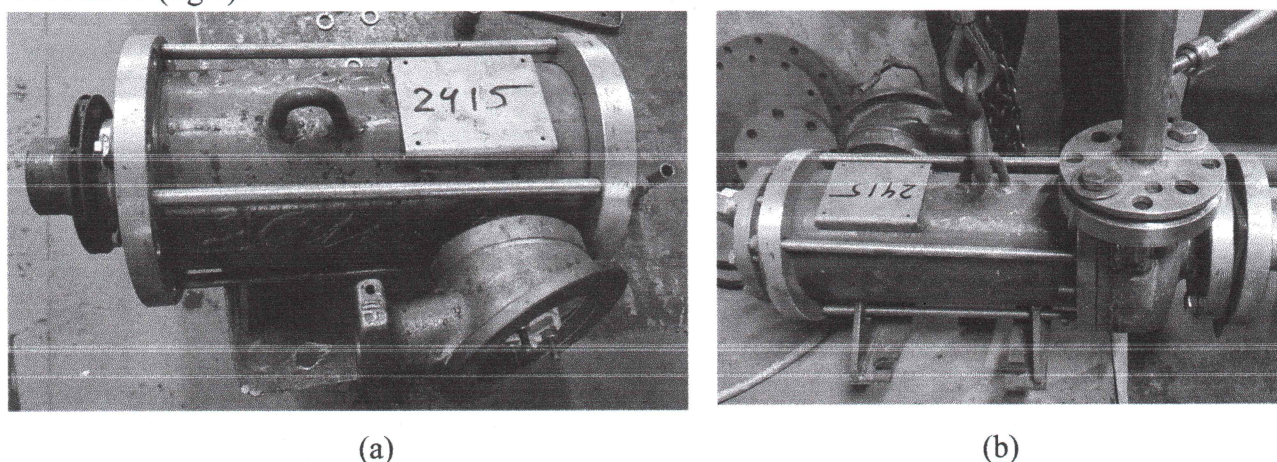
Testarea prototipului rotorului obținut: (a) Asamblarea rotorului pe pompă CH 6,3/20-1,1-2, (b) Testare pe standul experimental.
